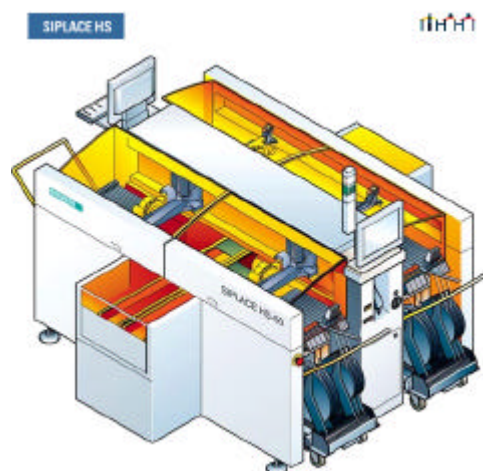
Exemplo de Máquina de Compôr Componentes SMT
